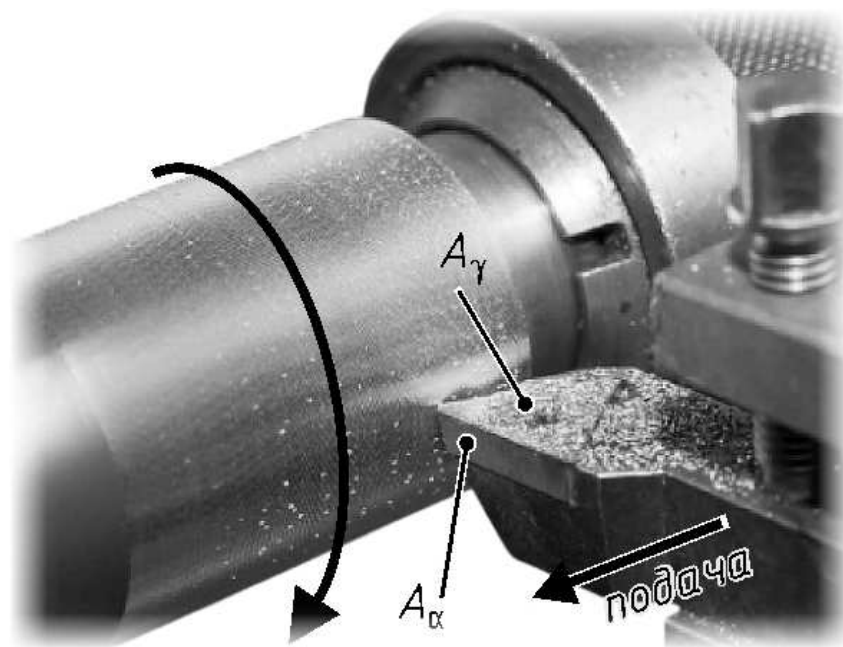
Заготовка, котру обточує токарний різець
